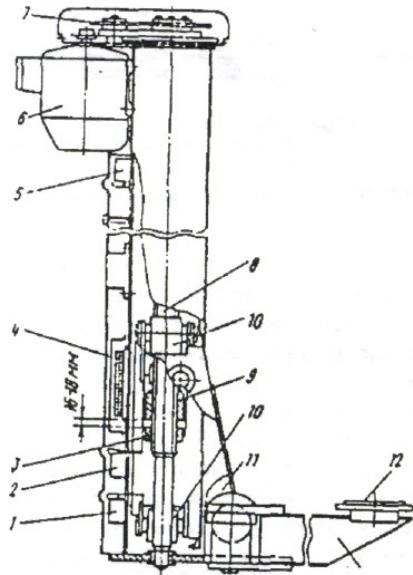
Левая стойка двухстоечного подъемника с электро механическим приводом: 1 - аварийный выключатель; 2, 5 - конечные выключатели; 3 - страховую гайку; 4 - электроклемник; 6 - электродвигатель; 7 - цепная передача; 8 - рабочий винт; 9 - грузовая гайка; 10 - опора винта; 11 - каретка; 12 - подхват; 13 - поворотная балка
